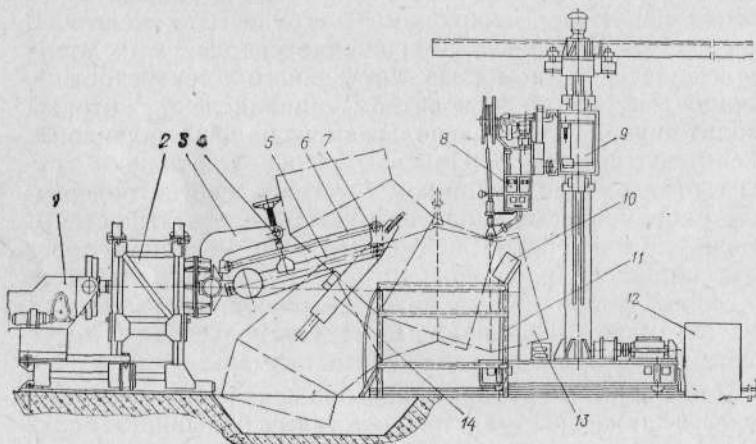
Установка УСО-1420 для сварки отводов  $D_y = 600\ldots 1400$  мм
